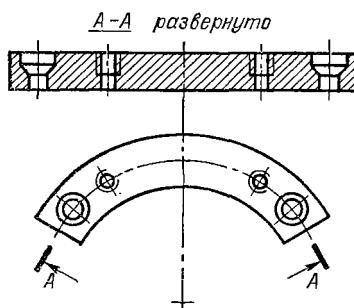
Разрез цилиндрической поверхностью, развертываемой в плоскость
